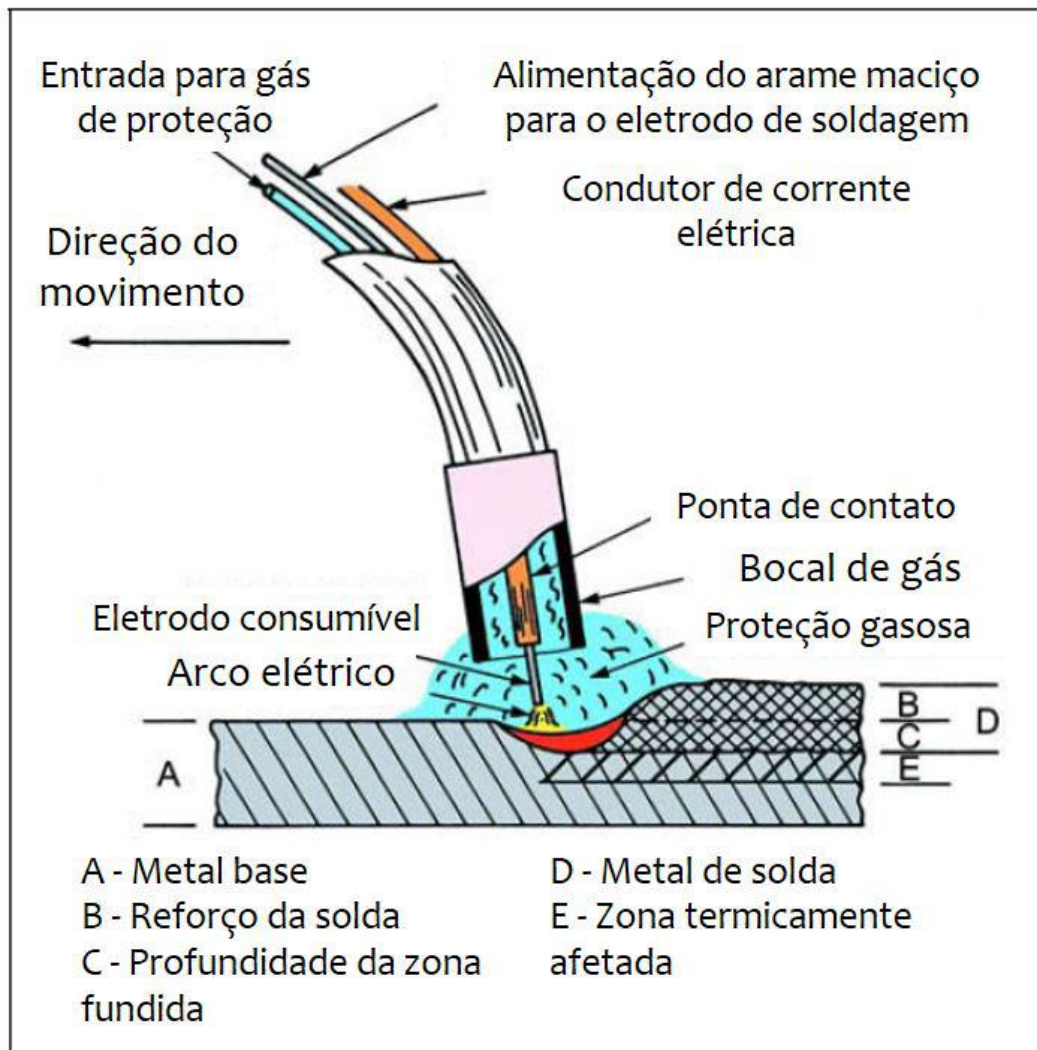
Desenho esquemático de uma operação de soldagem com GMAW (Adaptado de [28]).
